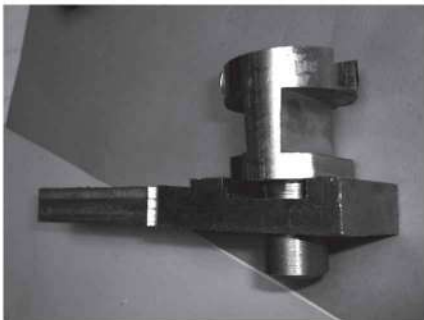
Montaje del portaburil con pieza principal y pieza ajustable
